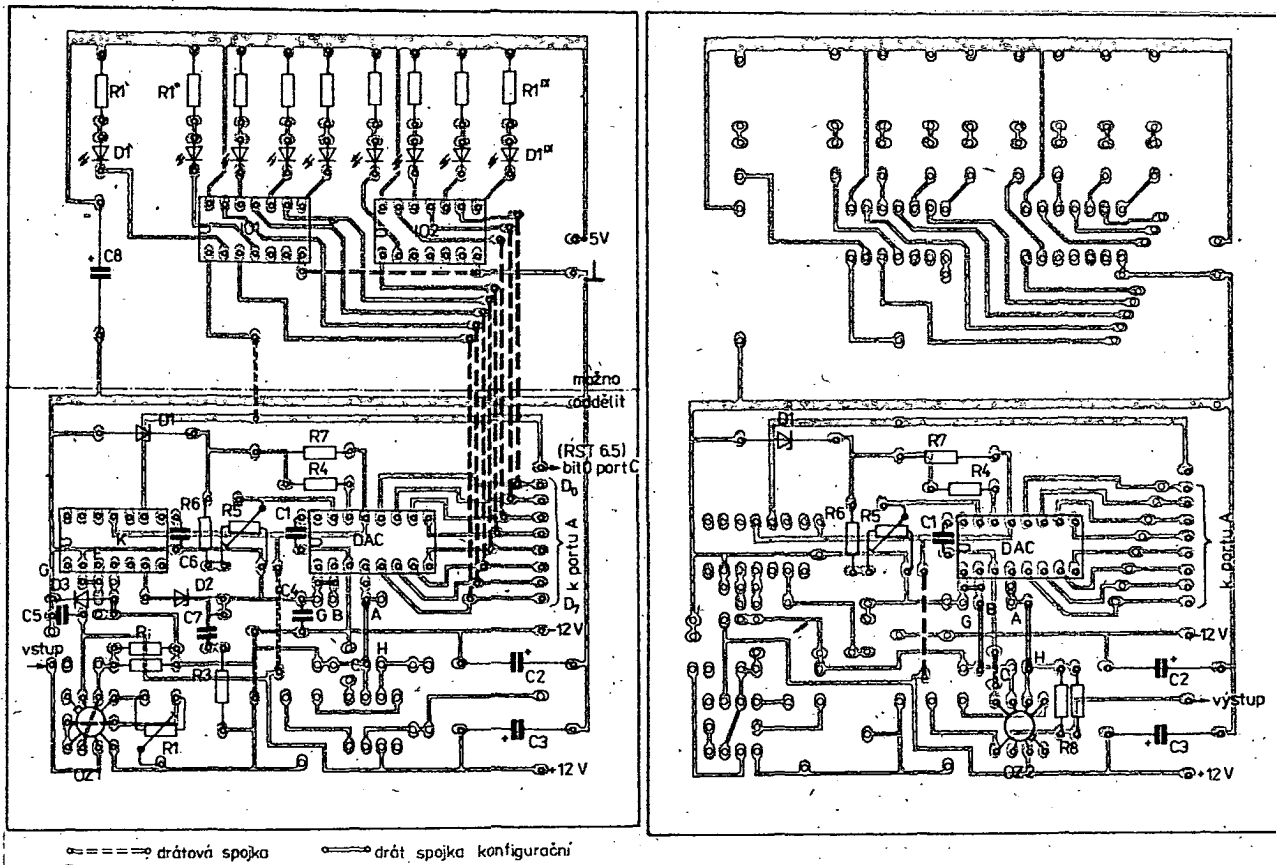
Zapojení univerzálního převodníku A/D a D/A s řízením účastí procesoru při převodu
